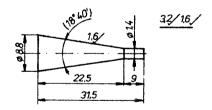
Kryt, poz. 6, materiál silon, 1 ks
